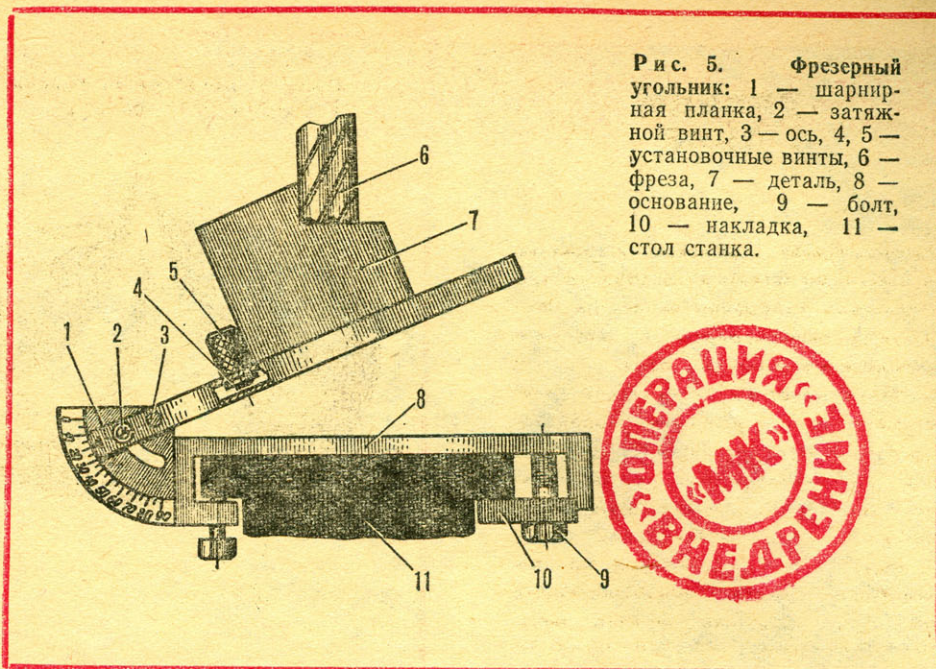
Фрезерный угольник: 1 — шарнирная планка, 2 — затяжной винт, 3 — ось, 4, 5 — установочные винты, 6 — фреза, 7 — деталь, 8 — основание, 9 — болт, 10 — наклейка, 11 — стол станка.
